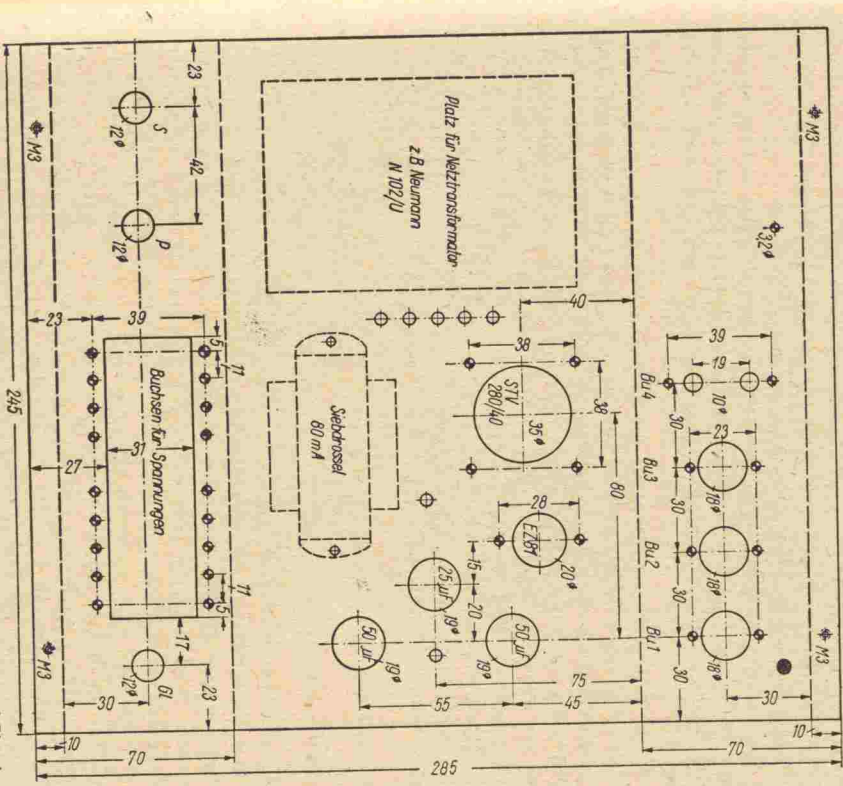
Maßskizze des Chassis mit Angabe der Befestigungslöcher, Durchführungen und Biegekanten. Die Breite des Buchsenausschnittes beträgt 100 mm
